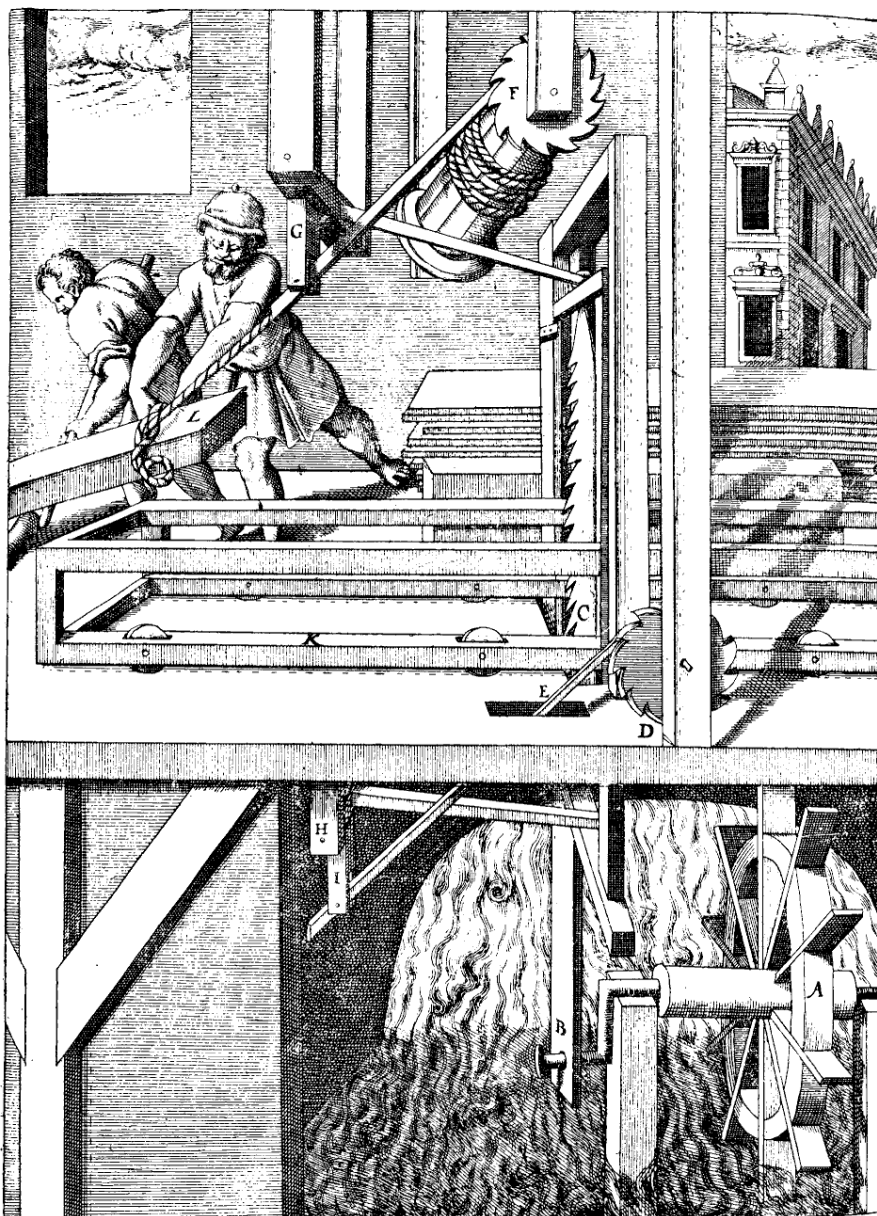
Machine à scier le bois au XVII^e siècle (BOCKLERI).
